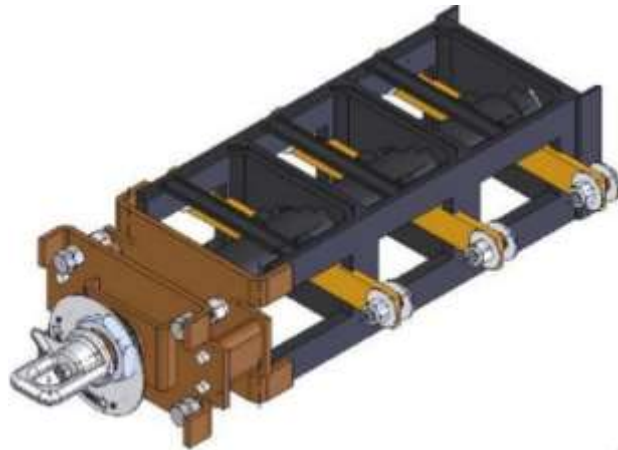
Partes del tanque de una caja de maniobras monofásica
